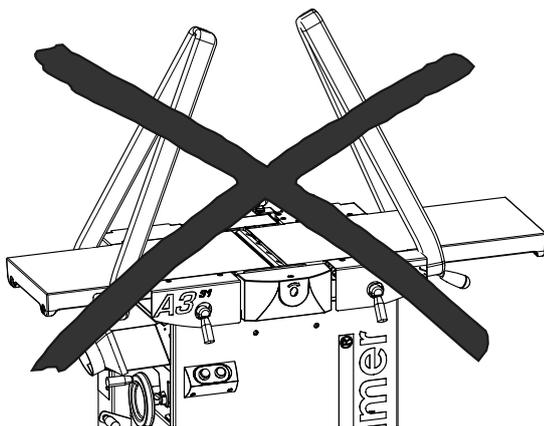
È vietato sollevare la macchina dai piani pialla.
